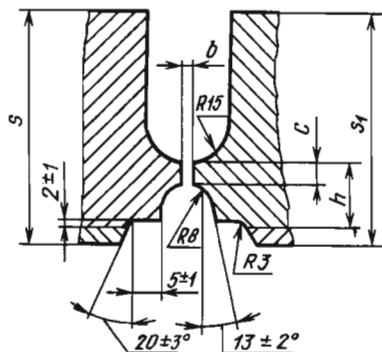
Разделка кромок стыкового сварного соединения двухслойной стали (С21)
